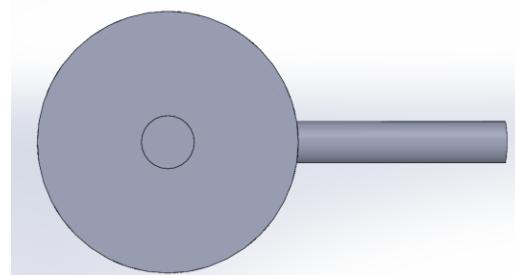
Vista superior del primer diseño de flotador hidráulico.
